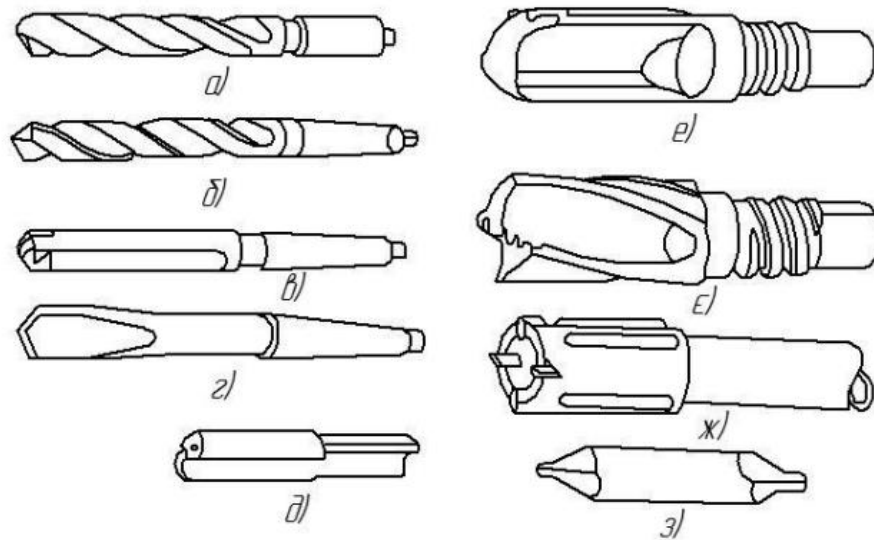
Види свердел: а, б – спіральні; в – з прямими канавками; г – перове; д – рушничне; е – однокромкове; є – двокромкове; ж – для кільцевого свердління; з – центрувальне
